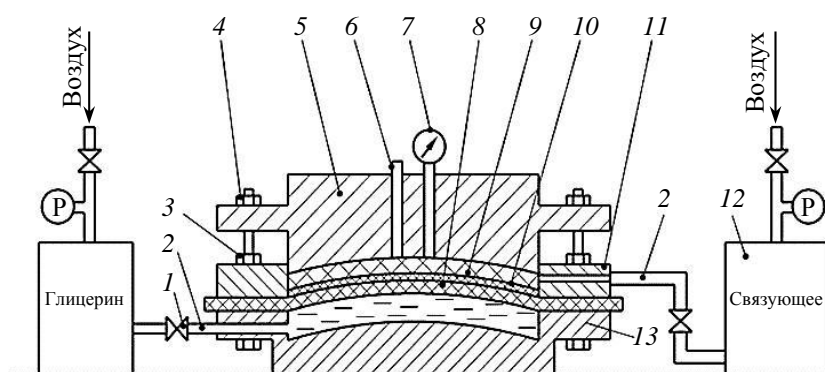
Схема приспособления для получения деталей двойной кривизны заданной толщины из ПКМ: 1 – редуктор; 2 – переходники; 3, 4 – гайки; 5 – оформляющая поверхность; 6 – штуцер; 7 – толщиномер; 8 – резиновая диафрагма; 9 – гибкая формирующая цулага; 10 – пакет непропитанной стеклоткани; 11 – рама; 12 – пропиточная установка; 13 – плита
